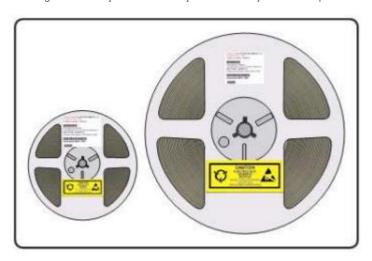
Posição de Identificação em um conjunto de componentes CKD embalado em Dry Pack
